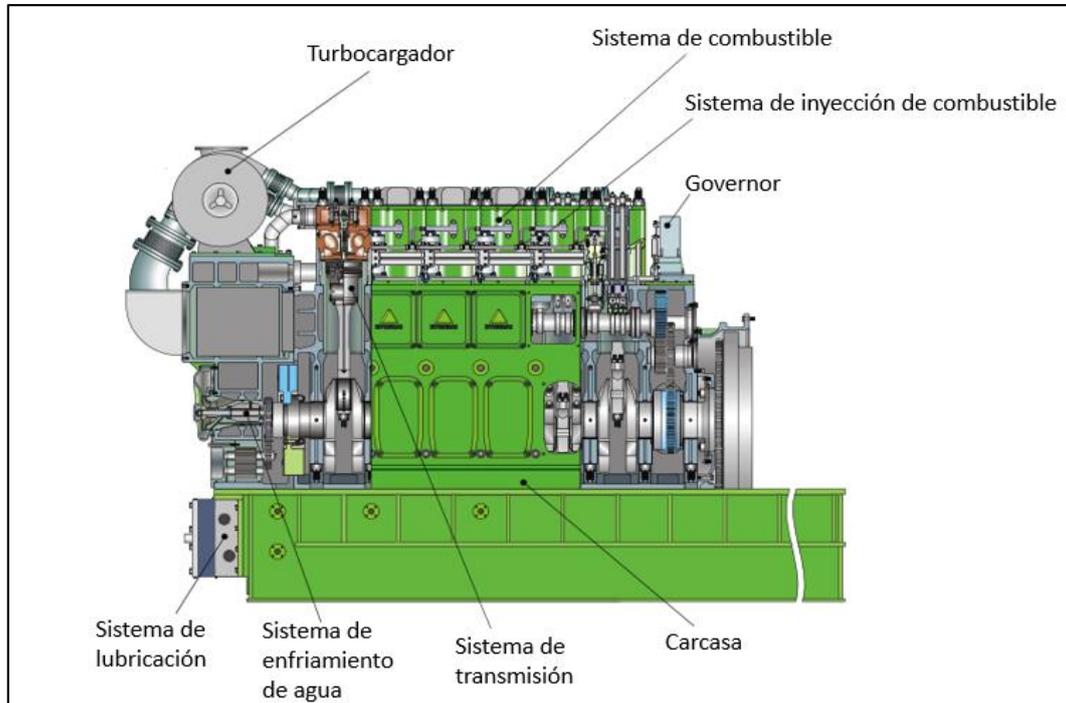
Motor de combustión interna y equipos auxiliares.
